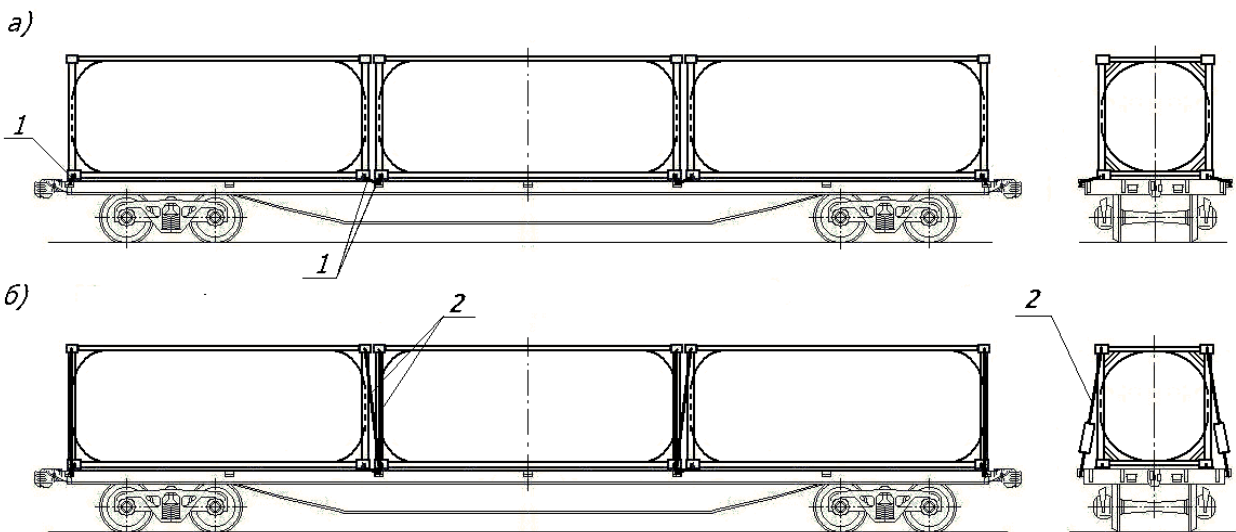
Дополнительное крепление контейнеров-цистерн на платформе для крупнотоннажных контейнеров:
